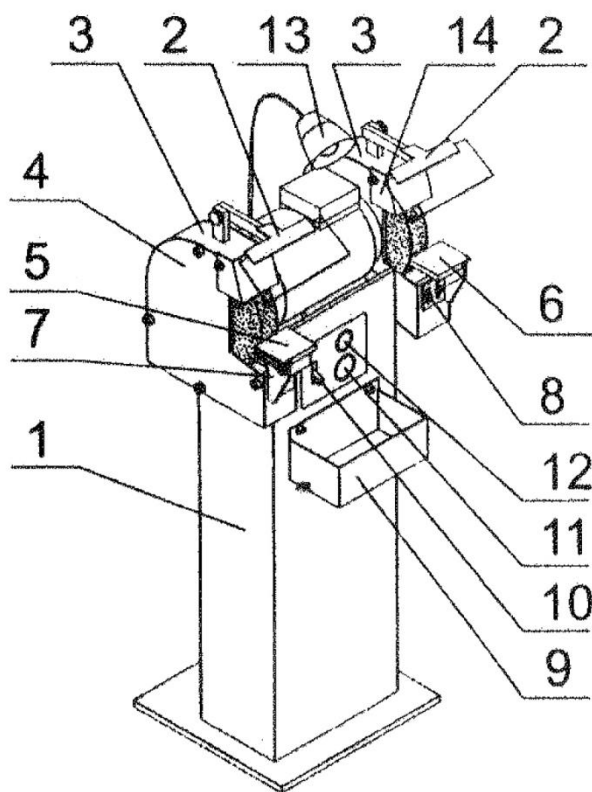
Схема точильно-шлифовального станка ТШ-2.20
